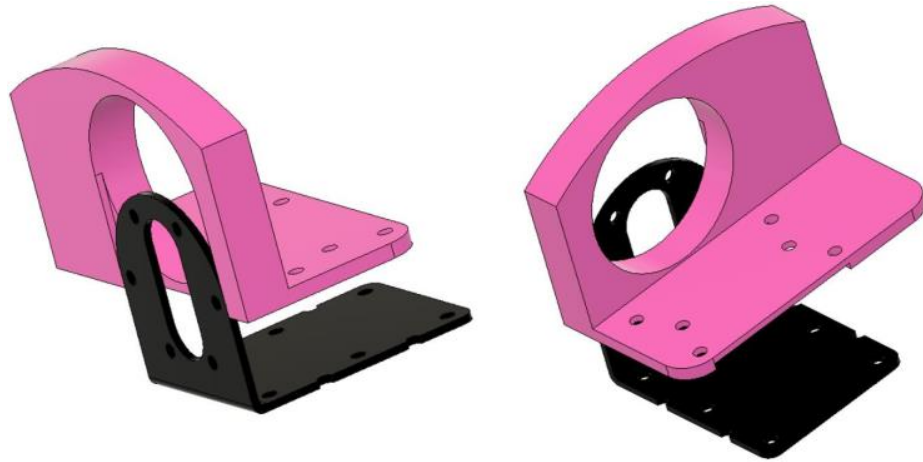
Flange usada na conexão entre elo e motor CC.
